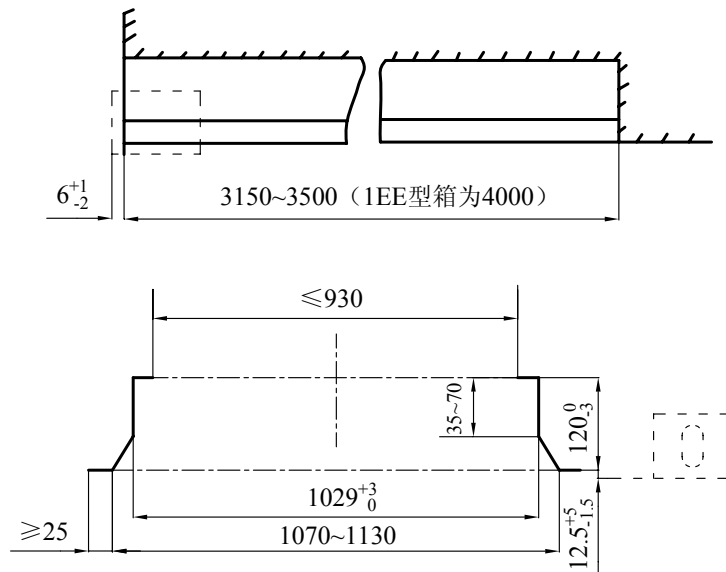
(1) 鹅颈槽断面图（单位: mm）
